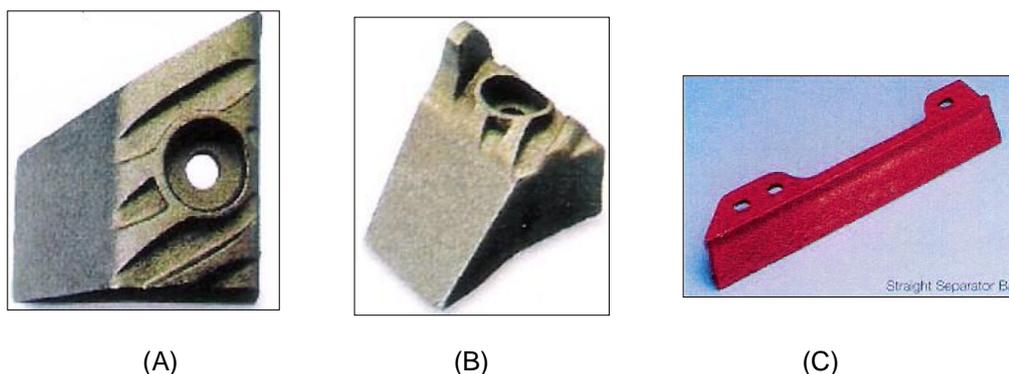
Componentes do rotor: (A) Gengiva lisa (B) Gengiva dentada (C) Barras separadoras.
